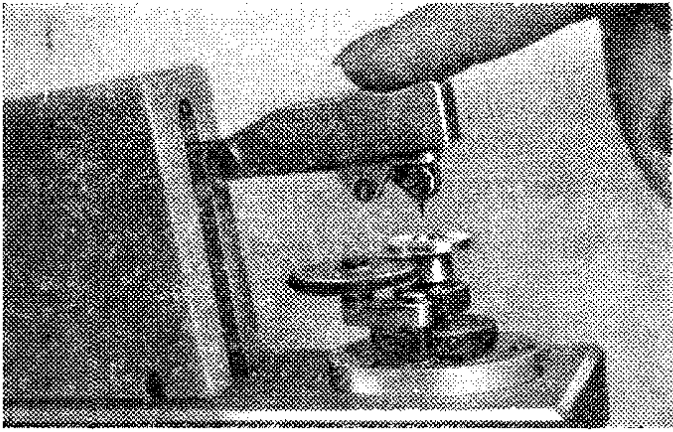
Отрезка внутреннего витка на приспособлении П82А
